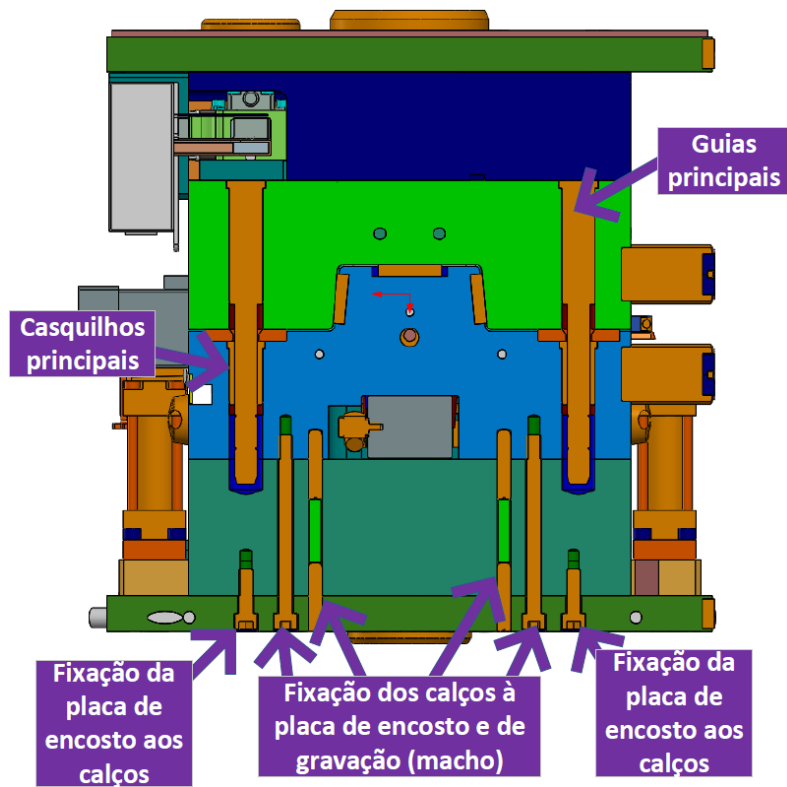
Fixações da placa de encosto do lado da extração à placa macho
